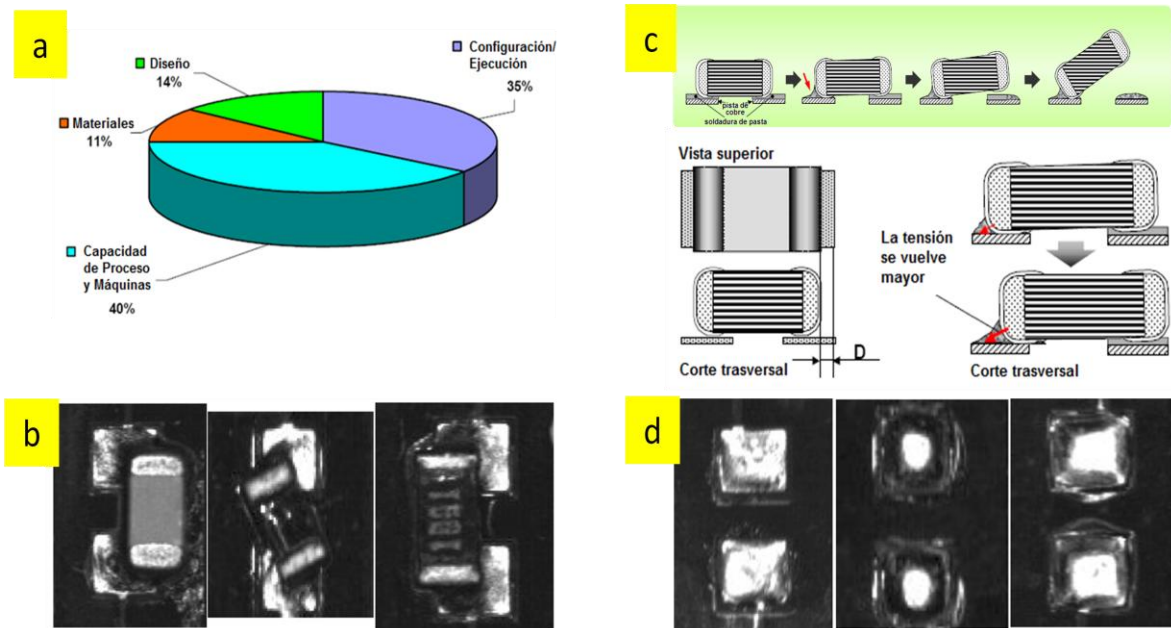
(a) Fuentes de defectos de SMT previos a soldar, (b) Componentes mal posicionados, (c) Corte transversal del mecanismo del efecto Manhattan en los SMDs, y (d) Componentes faltantes
